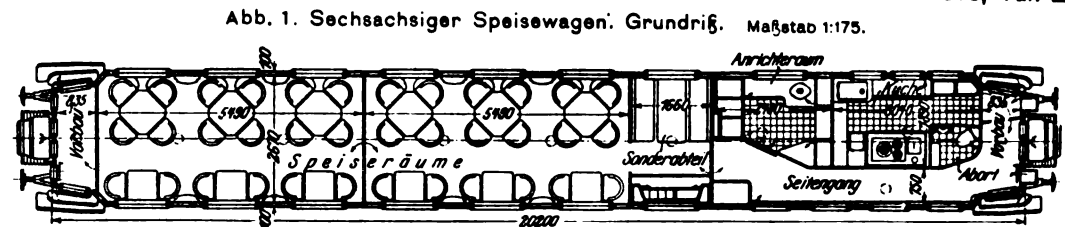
Sechssachsiger Speisewagen. Grundriß. Maßstab 1:175.
